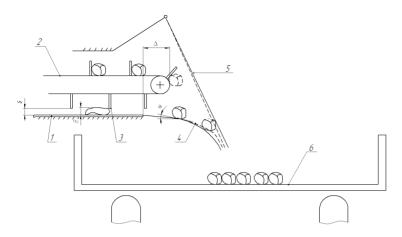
Принципиальная схема устройства для укладки кочанов в кузов транспортного средства в щадящем режиме: 1- поддон жесткий; 2- элеватор; 3- скребки; 4- лоток упругий прорезиненный; 5- фартук гибкий; 6- кузов транспортного средства
